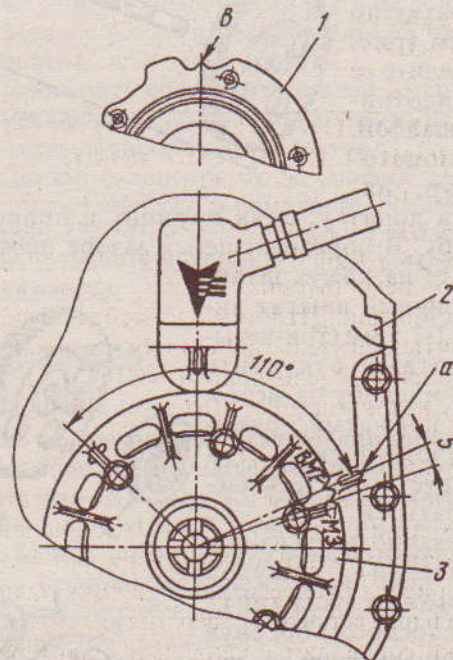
Расположение установочных меток: а - установочный выступ на крышке распределительных шестерен; в - выступ на корпусе центробежного маслоочистителя; ВМТ - верхняя мертвая точка; МЗ - момент зажигания; 1 - корпус центробежного маслоочистителя; 2 - крышка распределительных шестерен; 3 - крышка маслоочистителя
